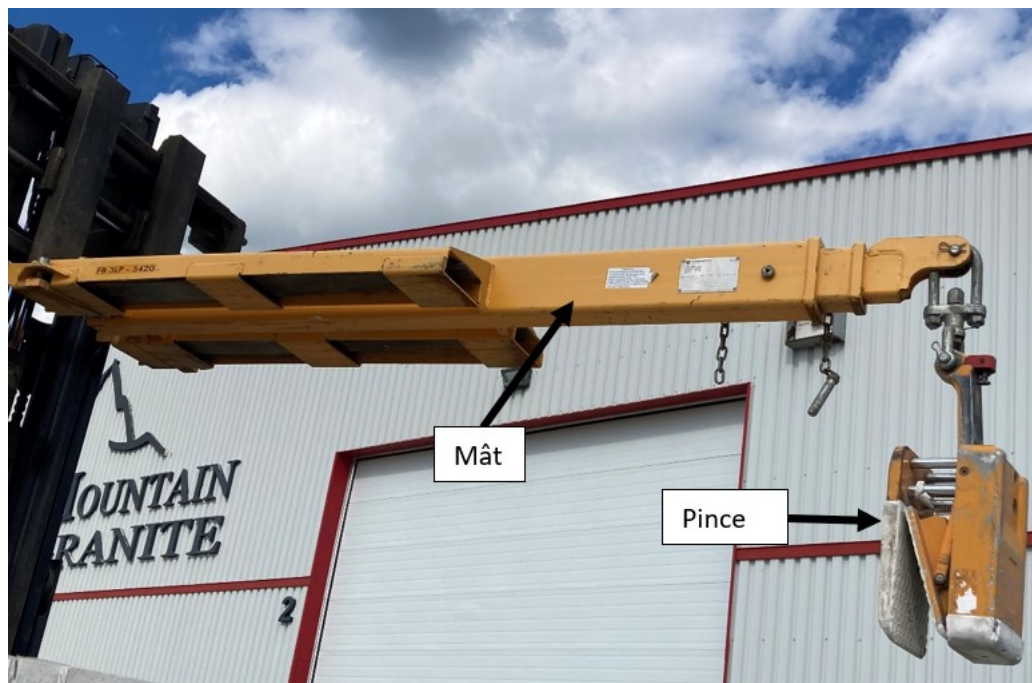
Mât sur les fourches du chariot élévateur et pince de levage de dalles
